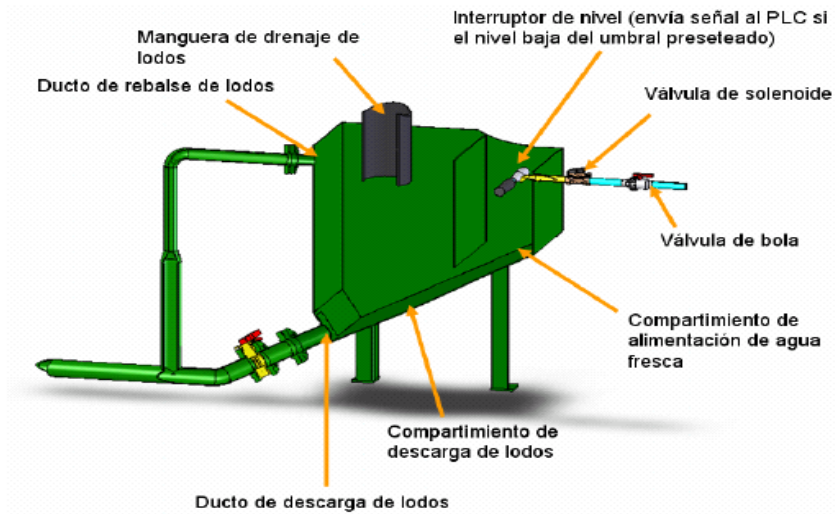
Esquema que muestra las partes que componen el estanque de vaciado.
